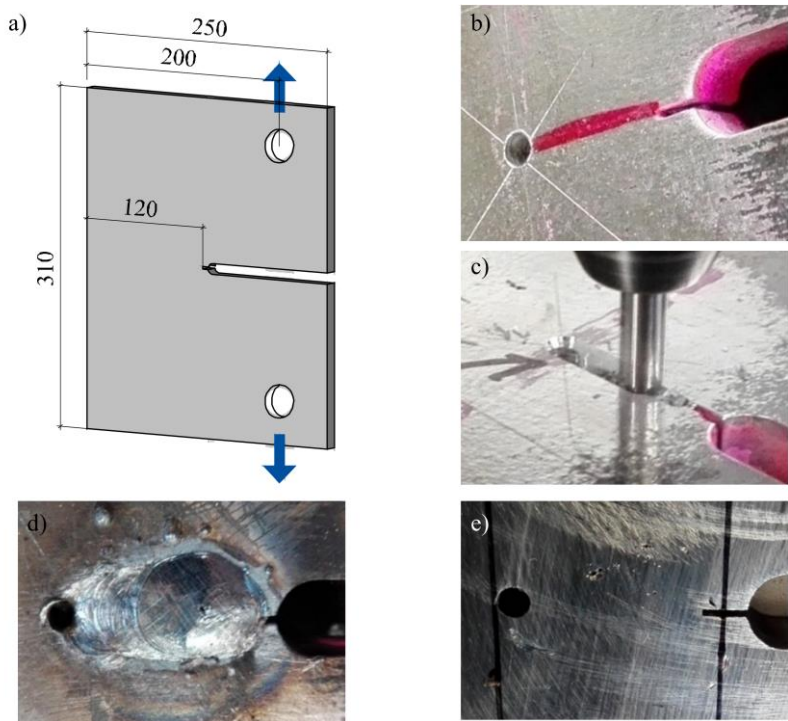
a) CT-Probe; b) Anbohren der Risspitze (Durchmesser: 4 mm); c) Ausfräsen des Risses (X-förmig); d) Reparaturschweißen (Lichtbogenschweißen); e) Abschleifen der Oberfläche
